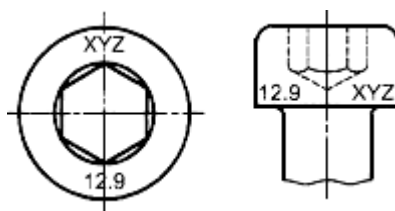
Примеры маркировки винтов с шестигранным углублением в головке
